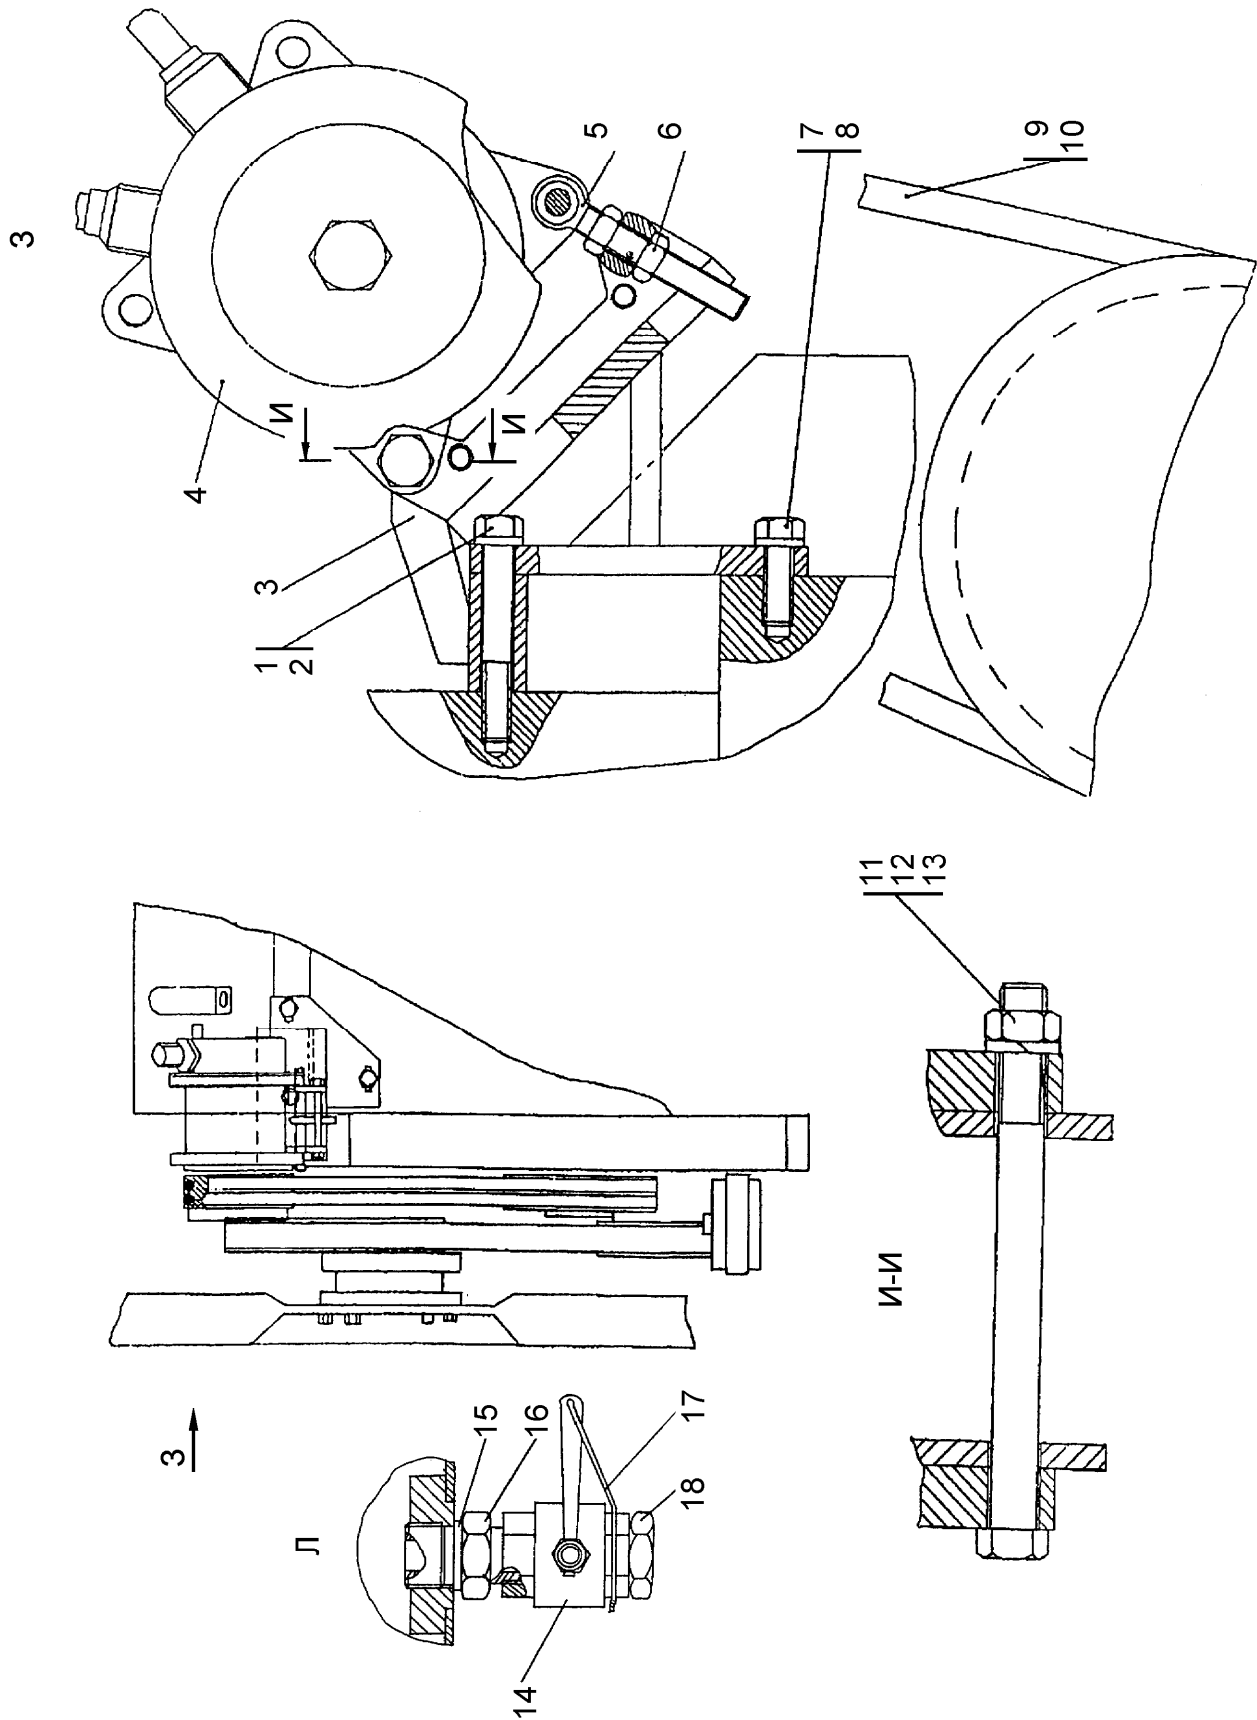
Установка двигателя М11-С «Cummins»
